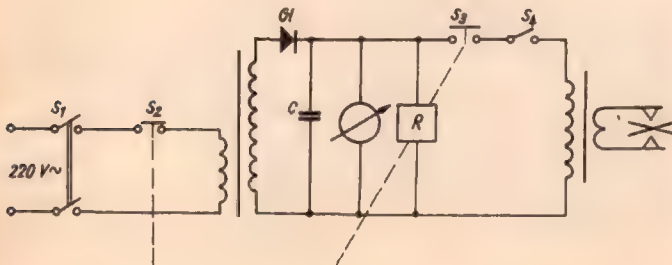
Links: Prinzip einer Impulsschweißmaschine.
